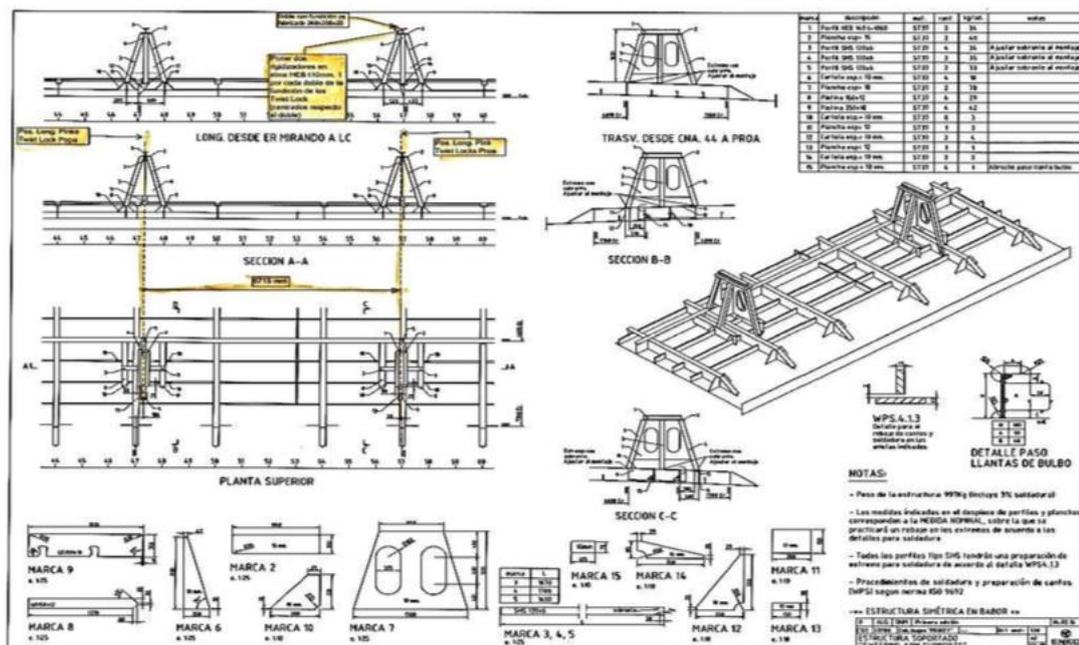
Planos modificación de la cubierta para la grúa de LAMOR. Merkleen 2016
